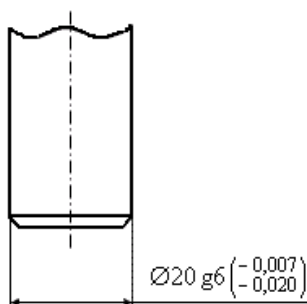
Обозначение поля допуска на диаметр вала
